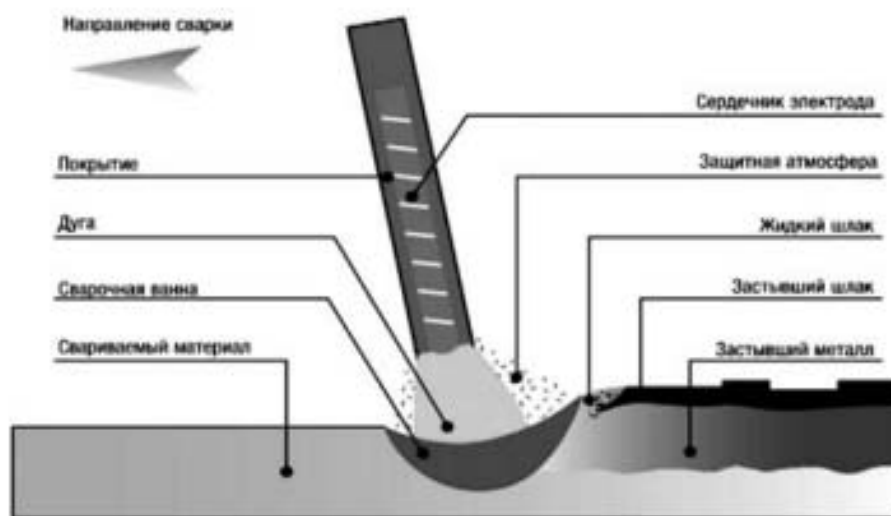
Схема ручной дуговой сварки
